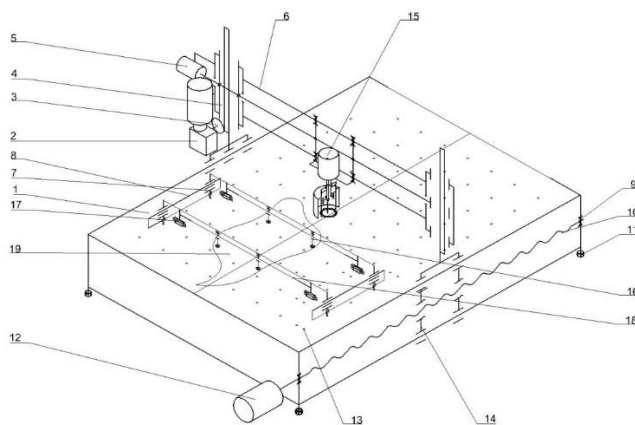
Кинематическая схема гравировально-раскройной лабораторной установки: 1 – алюминиевый стол; 2 - шаговый двигатель оси Z; 3 – зубчатое колесо; 4 - рейка; 5 – шаговый двигатель оси Y; 6 – Рама подвижного портала; 7 – шаговый двигатель дополнительных направляющих оси X; 8 – ходовой винт; 9 – шарикоподшипниковый узел; 10 – ходовой винт; 11 – регулируемые ножки; 12 – шаговый двигатель оси X; 13 – элементы крепления заготовки; 14 – портал с элементами
